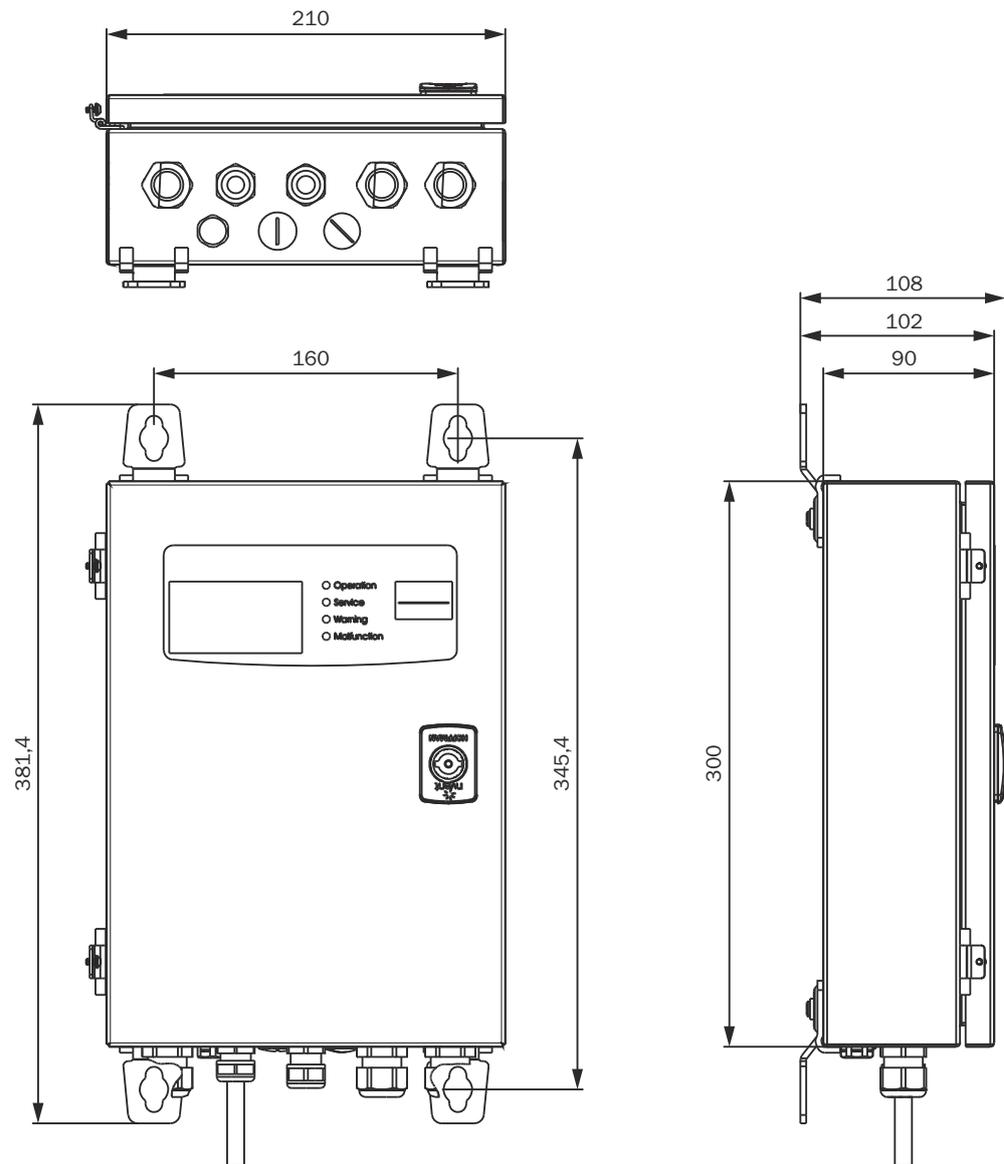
Steuereinheit AWE (Ausführung Stahlblechgehäuse), Maße in mm
